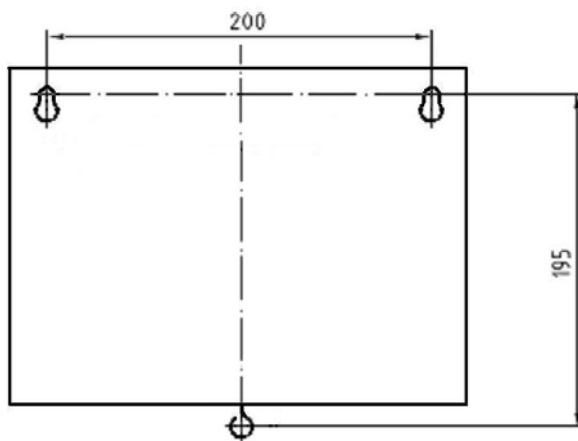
Крепление МИ-50 (установочные размеры)
